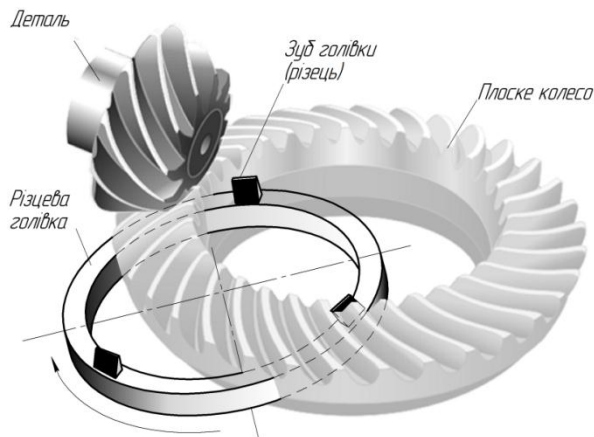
Схема нарізування конічних коліс з круговим зубом
